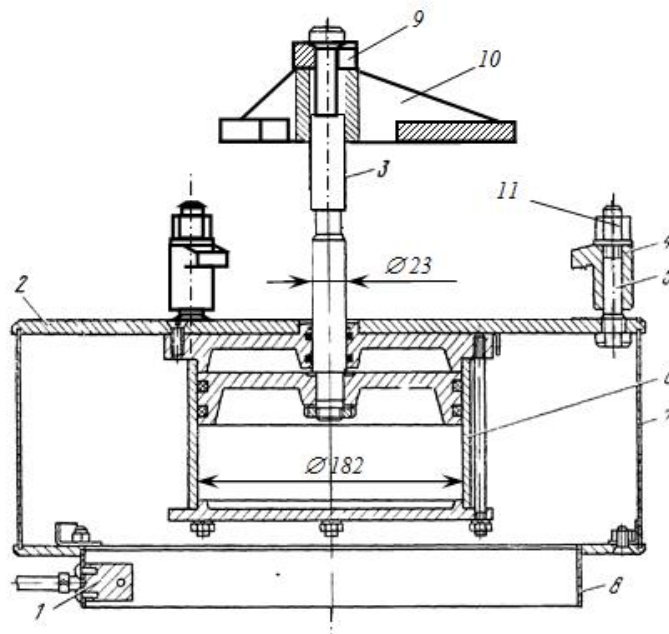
Пристрій для розбирання - складання та регулювання муфт зчеплення: 1 – ніпель трійника; 2 – станина пристрою; 3 – шток; 4 – утримувачі; 5 – направляючий болт; 6 – циліндр пневматичний; 7 – кожух; 8 – основа; 9 – кільце фіксатор; 10 – притискач; 11 - гайка
